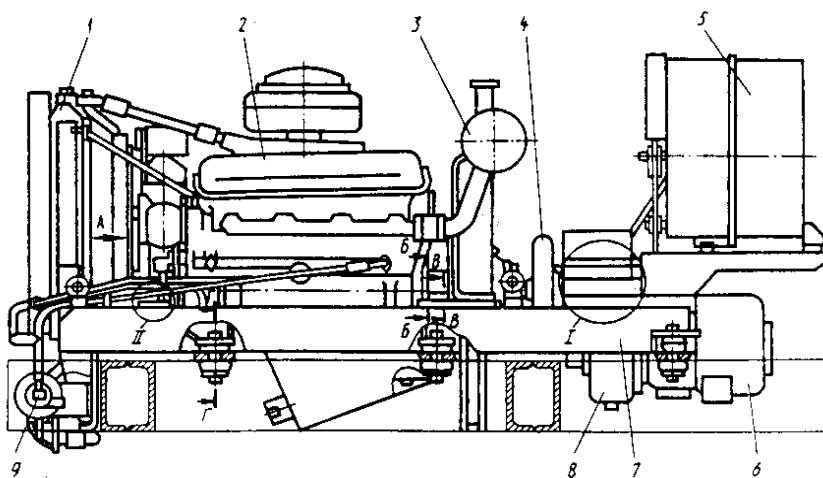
Силовая установка и силовое гидравлическое оборудование
